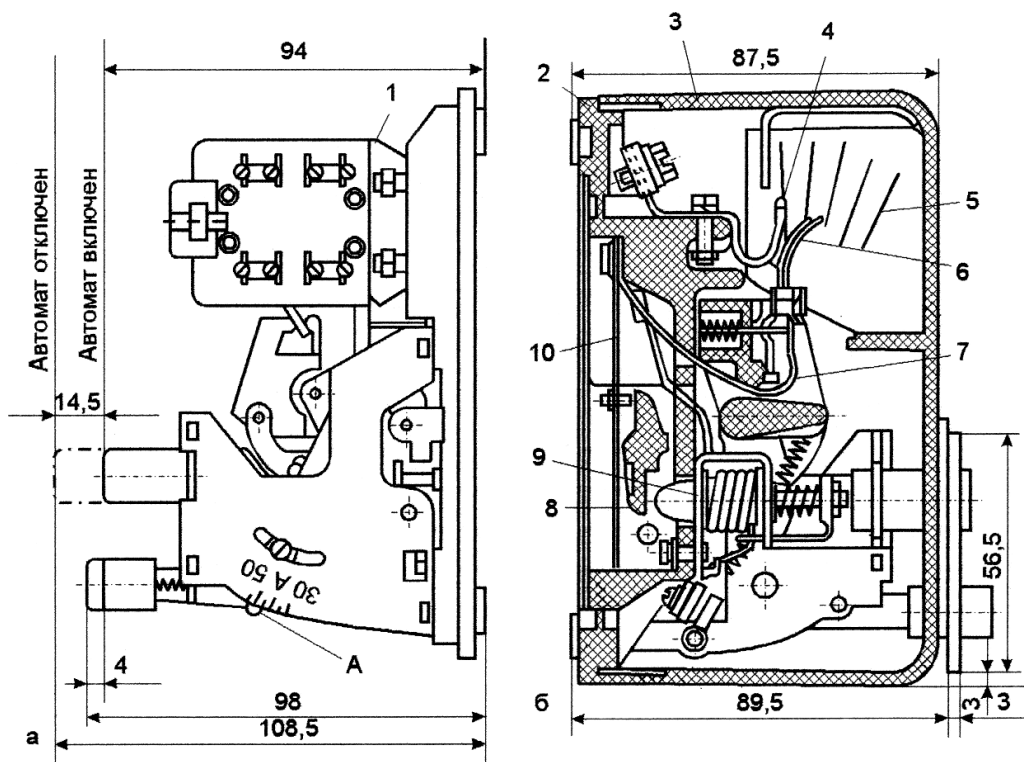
Устройство автоматического выключателя АП50: а — вид сбоку, б — в разрезе: 1 — блок с дополнительными контактами; 2 — цоколь корпуса; 3 — крышка; 4 — неподвижные контакты; 5 — дугогасительная камера; 6 — подвижные контакты; 7 — гибкий проводник; 8 — отключающая рейка; 9 — электромагнитный расцепитель; 10 — тепловые расцепители
